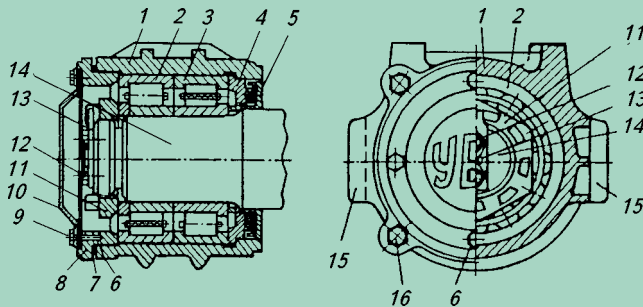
Букса грузового вагона с двумя цилиндрическими роликовыми подшипниками
